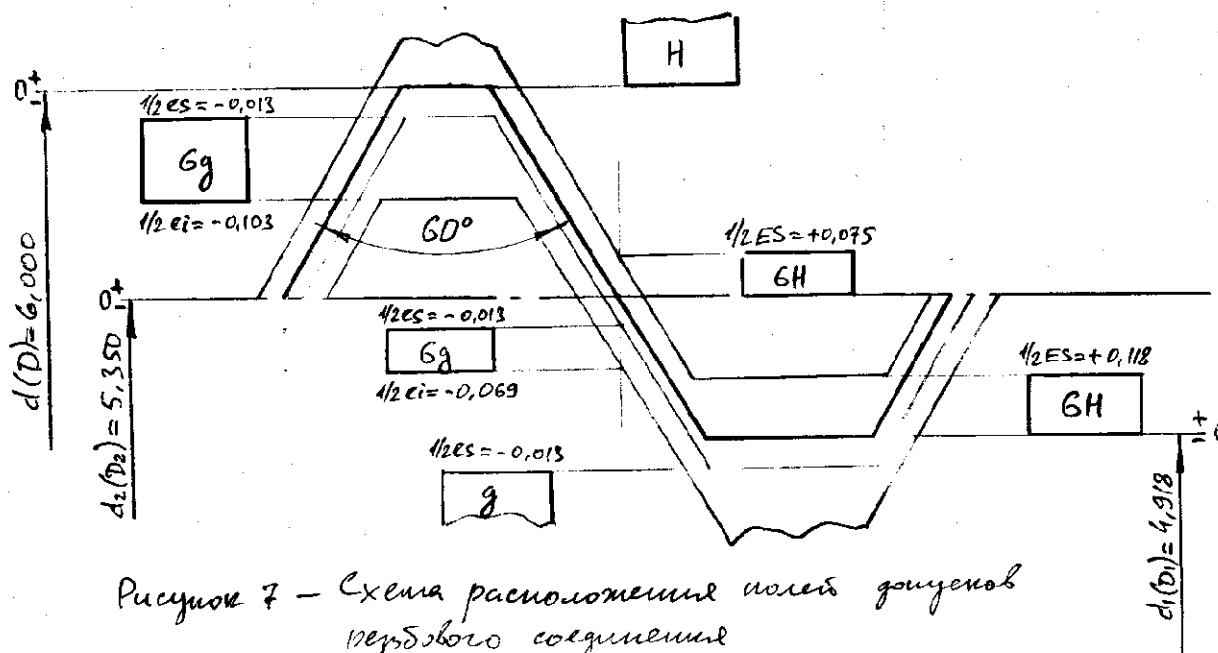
Схема расположения полей допусков резьбового соединения
